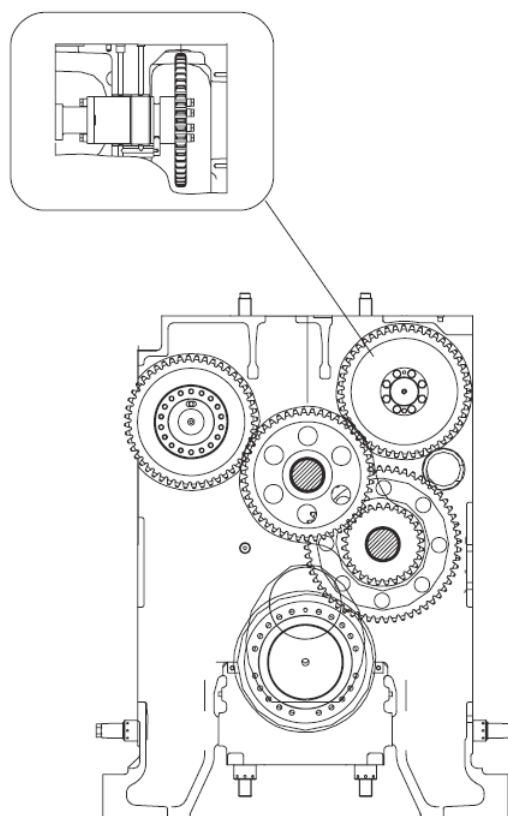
Зняття зубчастого колеса і опорної плити підшипника.
